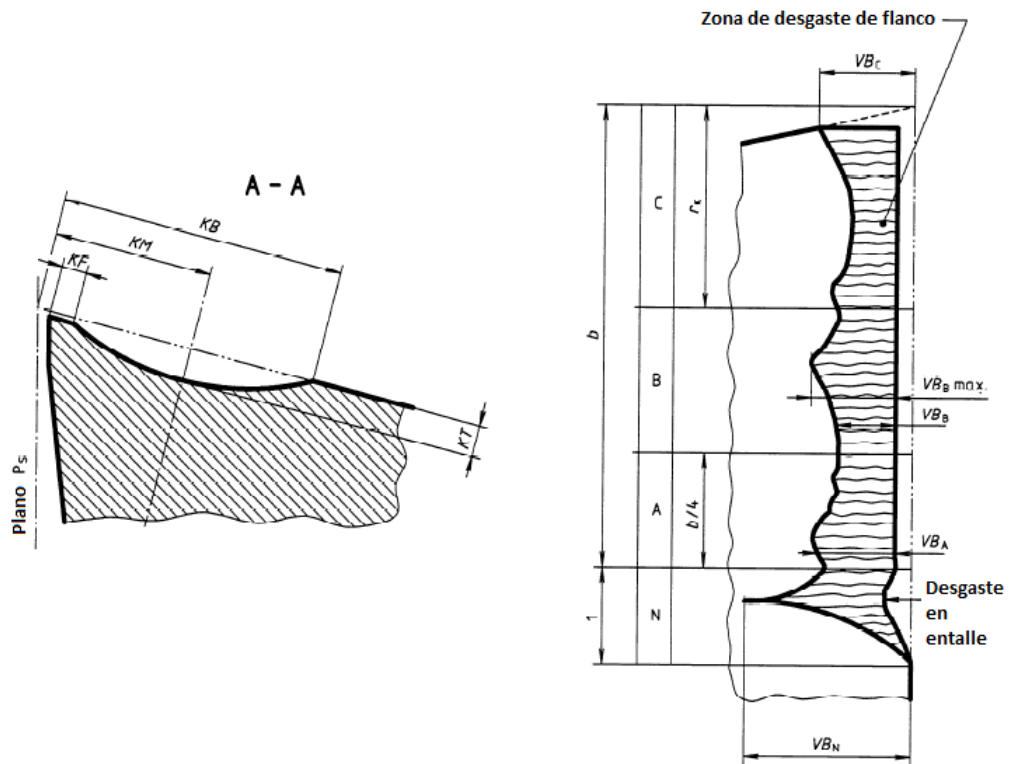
A lado derecho, desgaste de flanco de herramienta. A lado izquierdo corte en sección para una vista de la profundidad del cráter [31].
